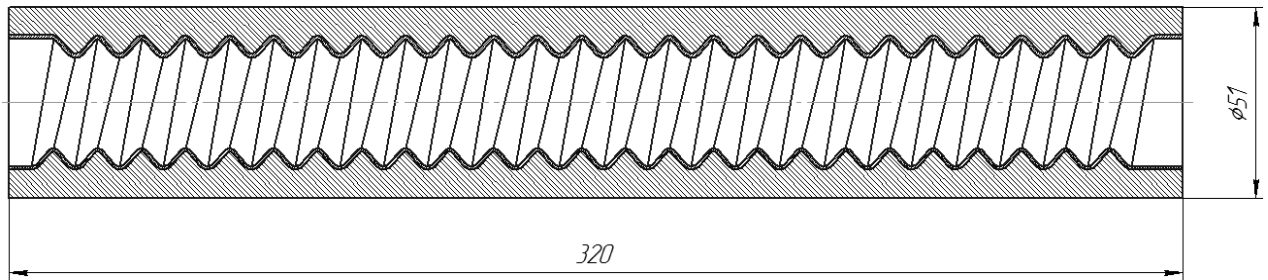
Поздовжній розріз заготовки труби калориметра
